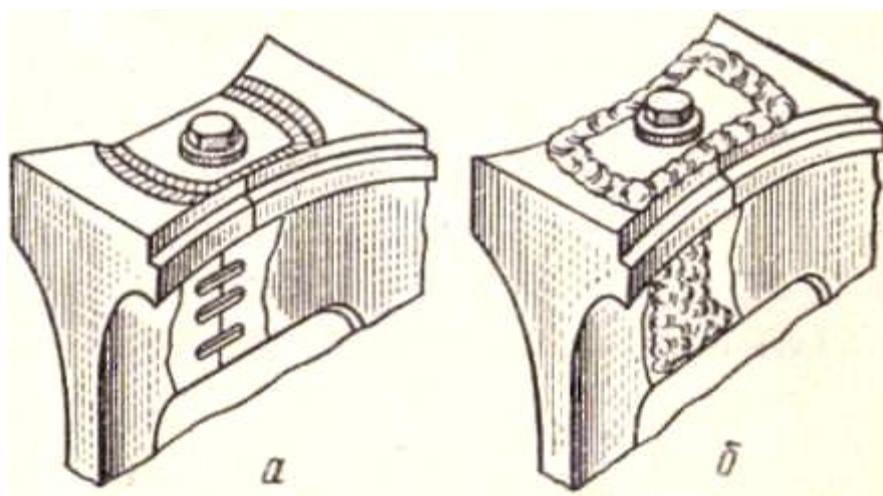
Підготовка тріщини в перемичці між циліндрами до заварки (а) і перемичка після заварки (б).
